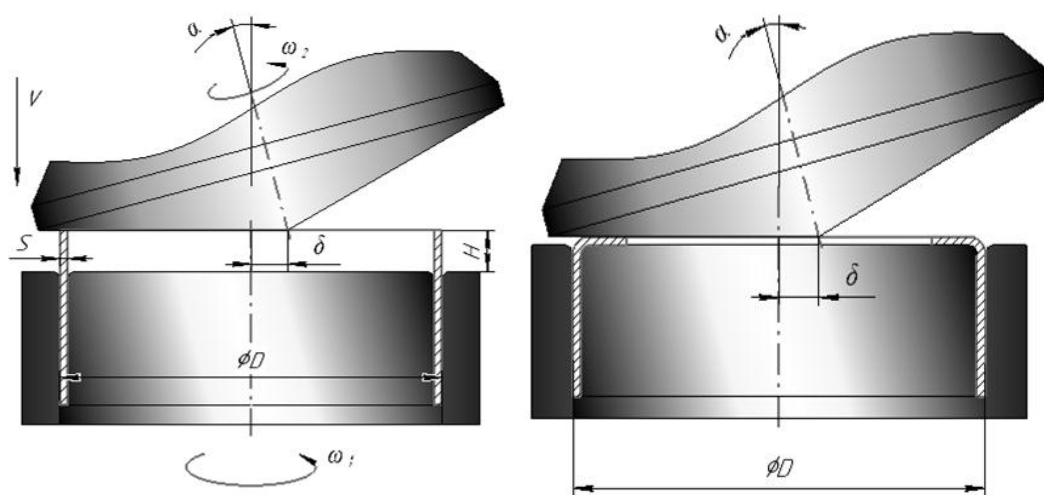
Схема торцевой раскатки трубной заготовки при формировании внутреннего фланца
